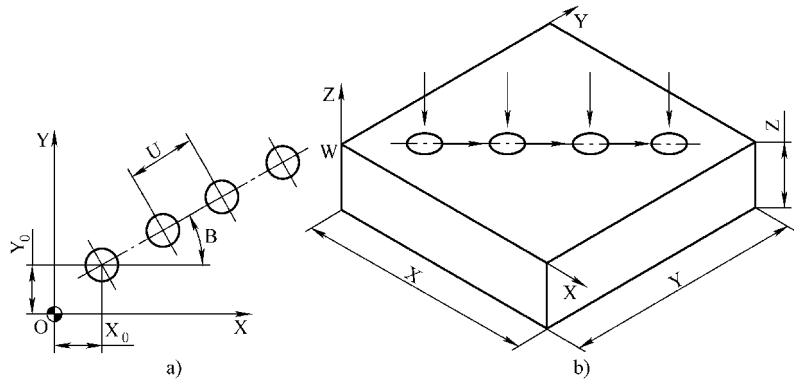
直线点阵孔群钻削加工刀具路线示意图
